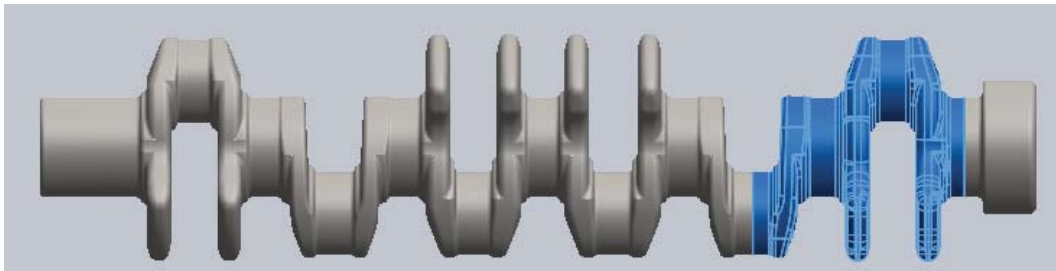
Выделение четвёртой части из детали коленчатого вала
